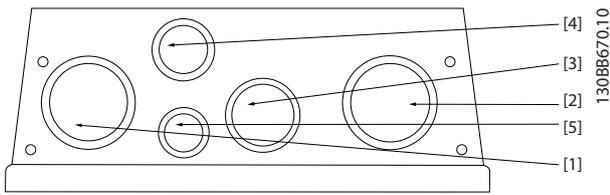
B2 - Kabeleinführungsöffnungen mit Gewinde IP55
